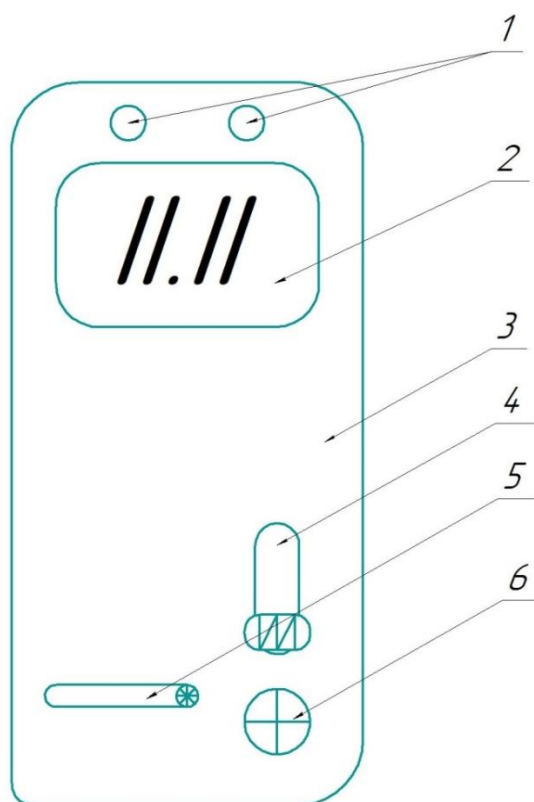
Загальний вигляд приладу для вимірювання рівня глюкози в крові: 1 – Пристрої вводу; 2 – Дисплей; 3 – Корпус; 4 – Ланцетний пристрій; 5 – Блок тест-смужок; 6 – Кнопка керування.
